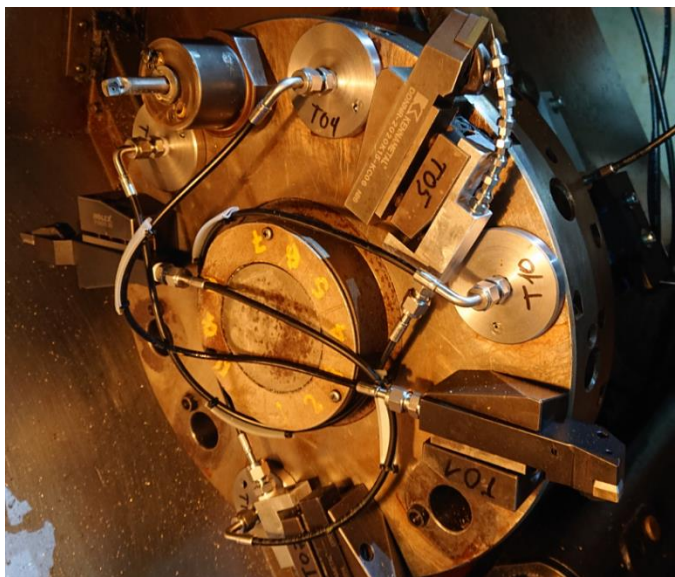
Komplett bestückter Werkzeugrevolver mit kryogener Kühlzuführung
